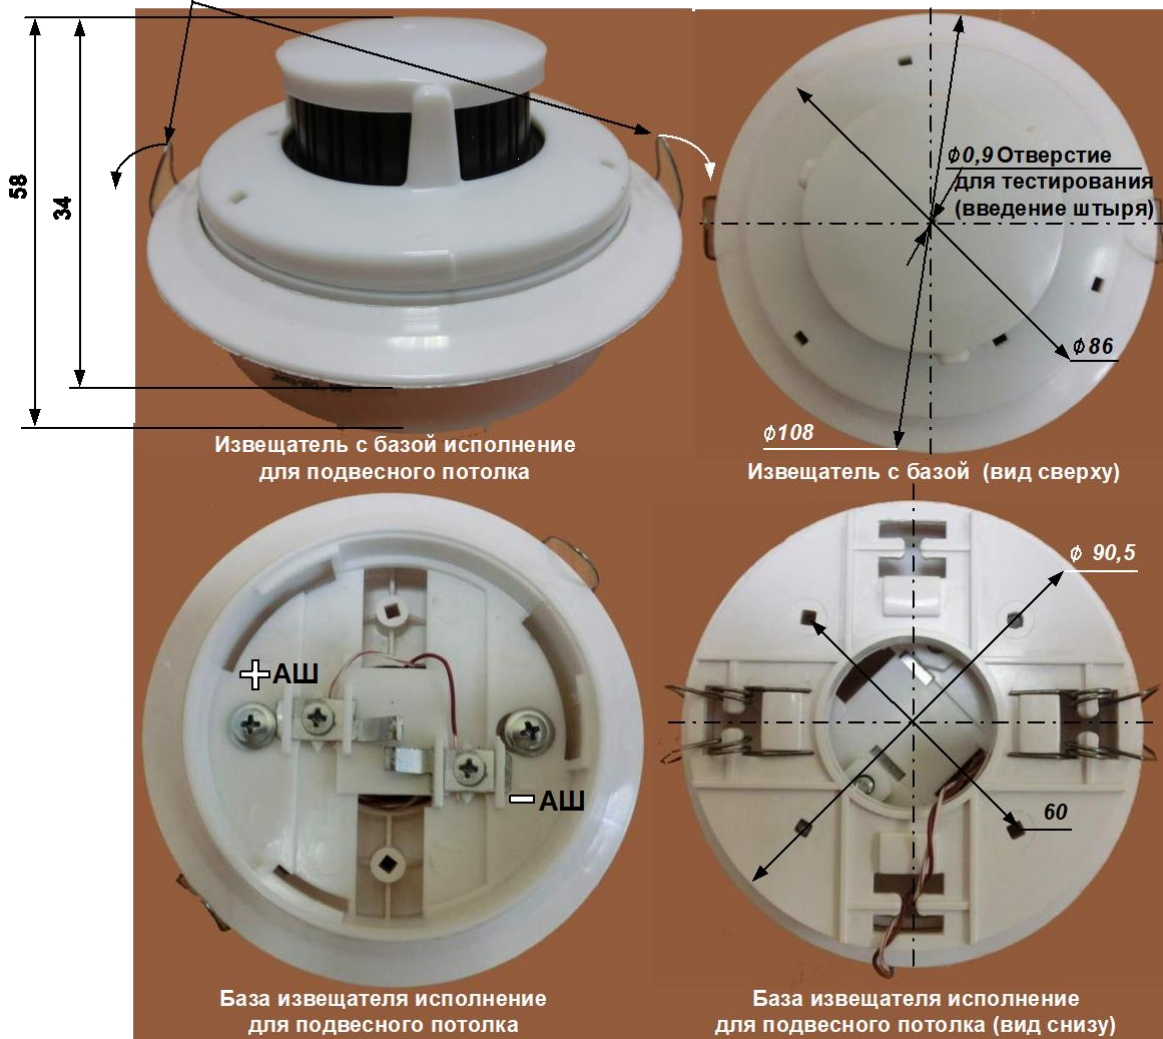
АТИ (блок извещателя, база для подвесного потолка). Габаритные и присоединительные размеры.
